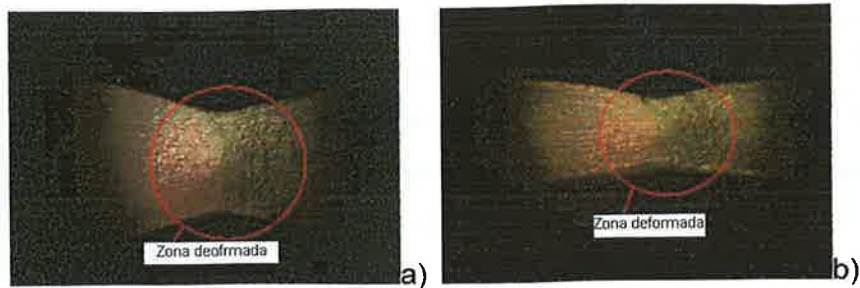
Uniones soldadas por fricción ensayadas en la barra Hopkinson a una velocidad de impacto de $v=25$ m/s.
